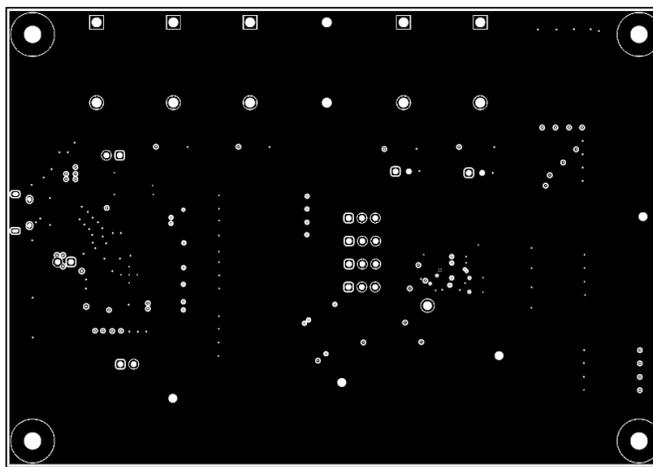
AMC6V704EVM PCB 中层 4 布局 (接地平面)
